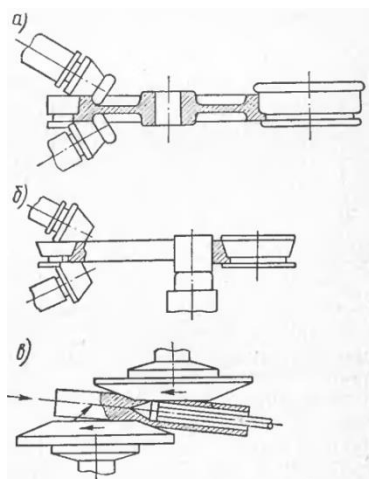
Клетки с косо расположенными валками: а, б – колесопрокатные, в – для прошивки труб
